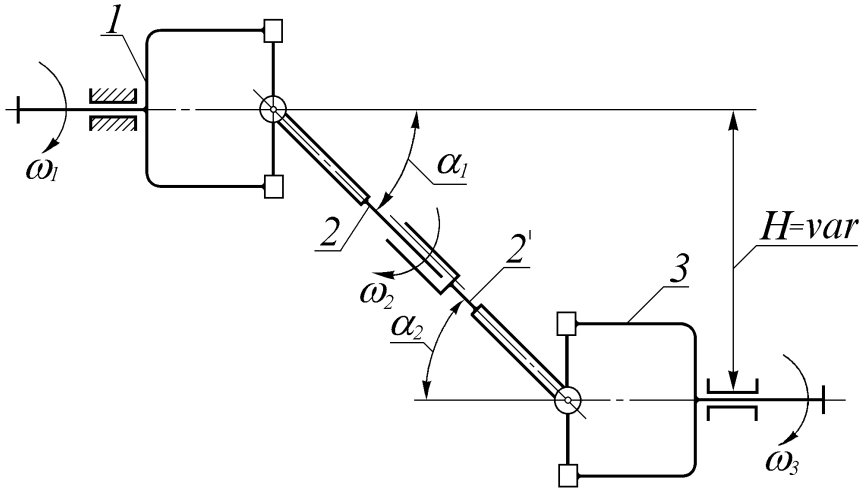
Кінематична схема здвоєного шарніра Гука
